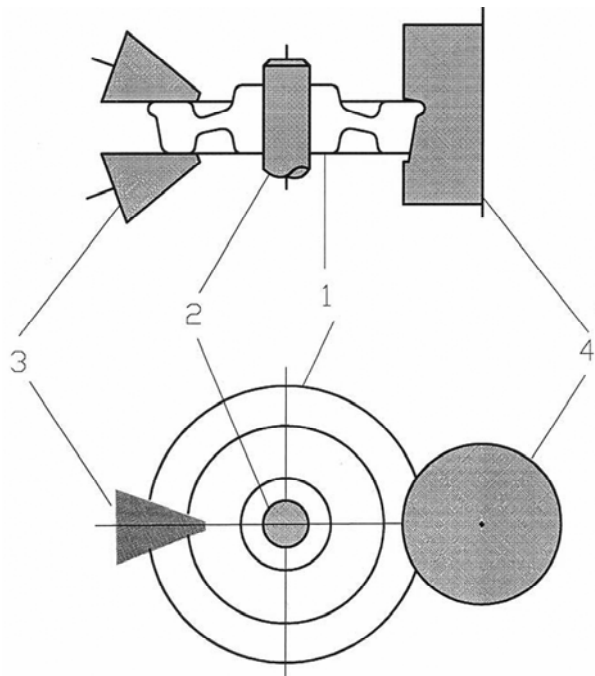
Схема прокатки колеса на кольцебандажном стане:
